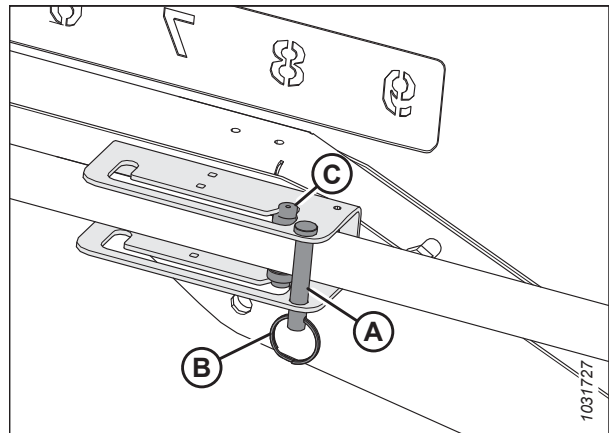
Cilindro del brazo izquierdo: Posición de retroceso
